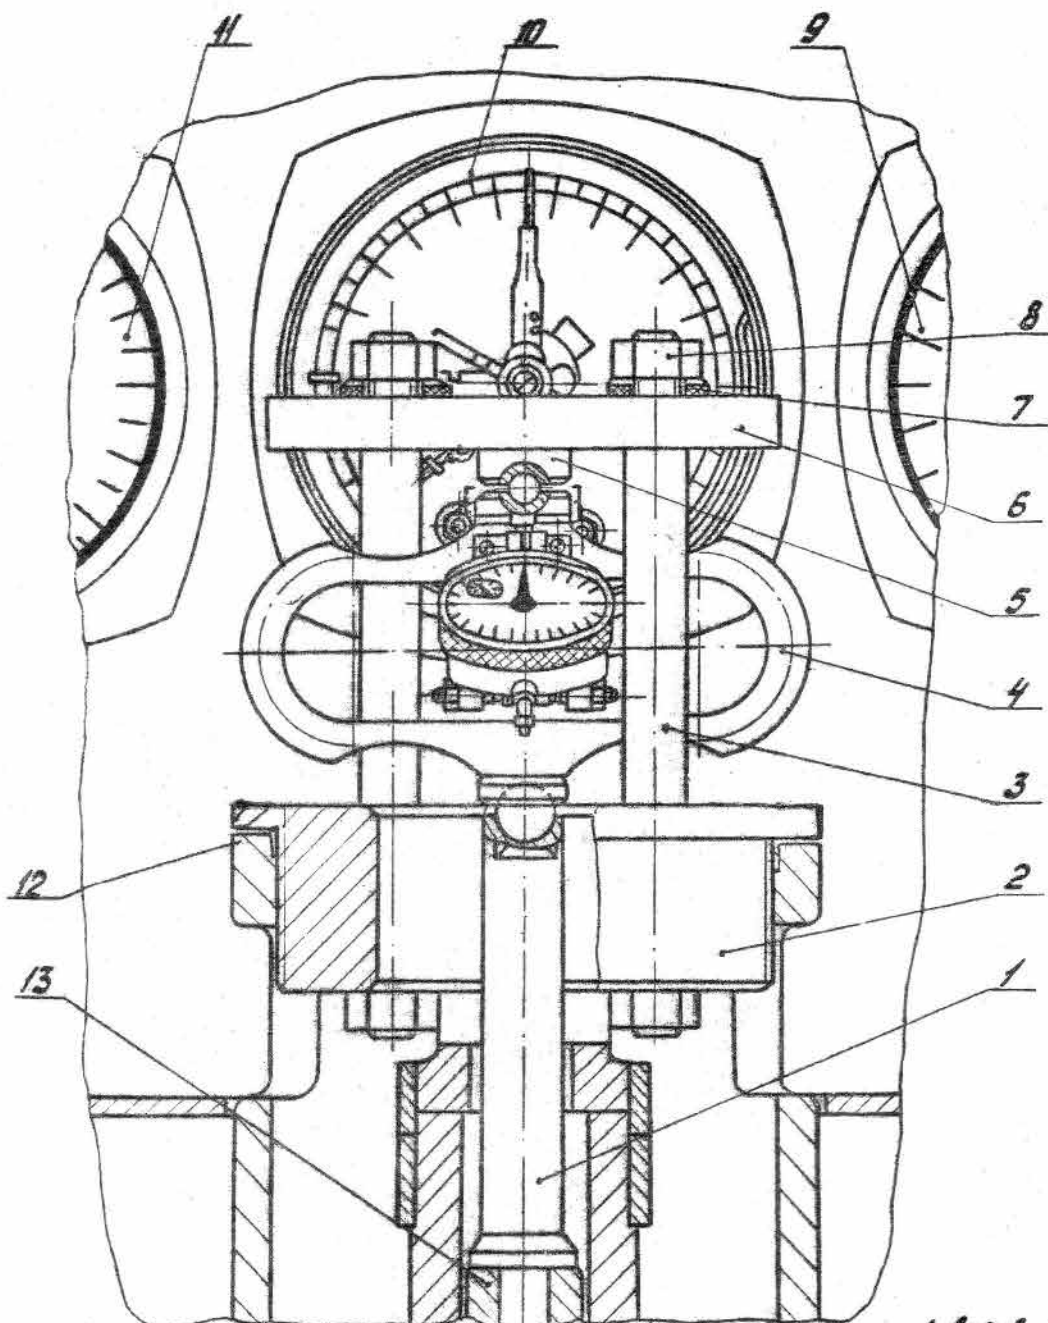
Схема установки приспособления для поверки силоизмерителей выдавливания
